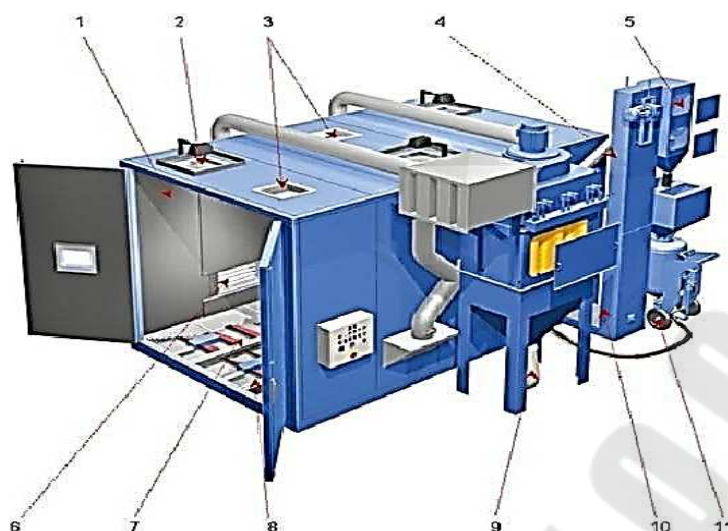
Схема дробеструйной камеры с системой сбора дробы
